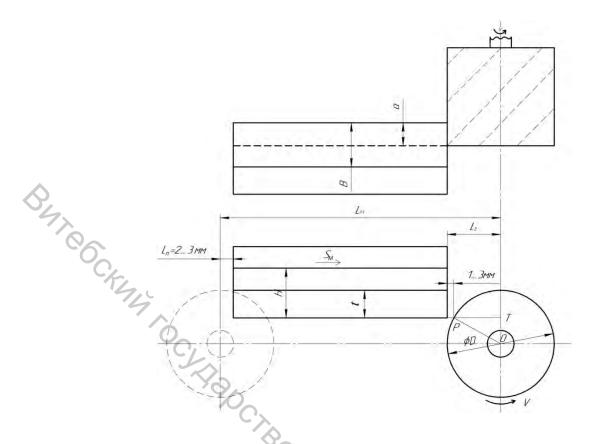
Схема определения длины рабочего хода при фрезеровании уступов концевой и торцовой фрезами
